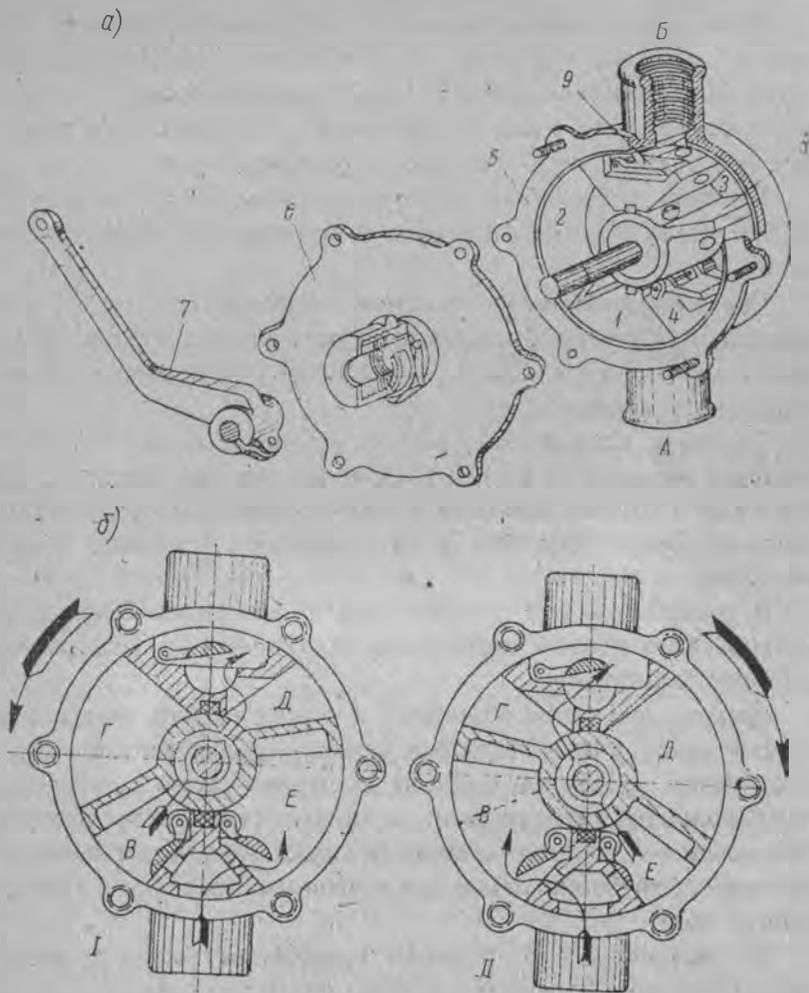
Ручной топливный насос РНА-1А (альвейер): а — устройство насоса; 1, 2, 3, 4 — полости насоса; 5 — корпус насоса; 6 — крышка; 7 — поводок; 8 — крыльчатка; 9 — клапан нагнетания; А — вход горючего; Б — выход горючего; б — схема работы ручного насоса
